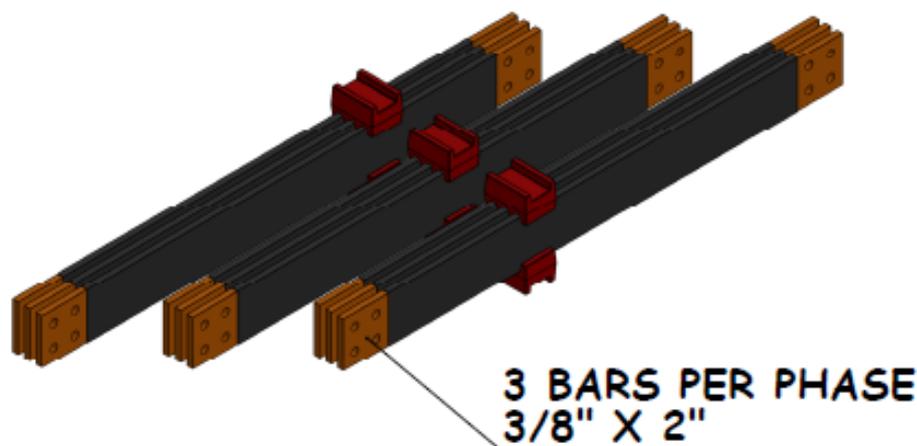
"Configuración del barraje" VISTA ISOMETRICA
